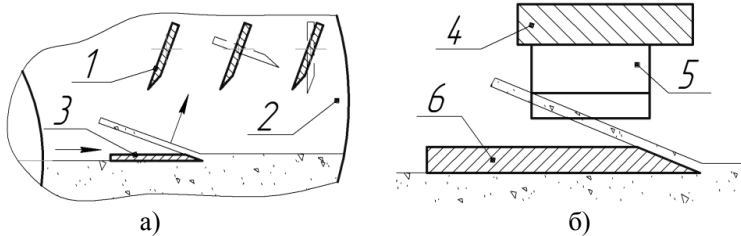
Принципові схеми пристроїв для підвищення продуктивності кутера: а) - статичного (вид зверху); б) - динамічного.
